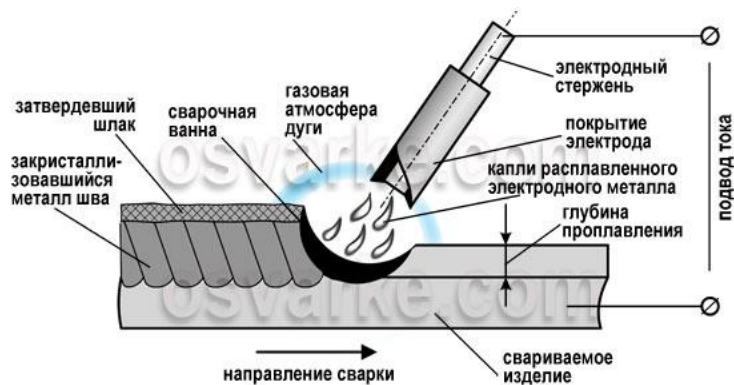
Принципиальная схема ручной дуговой сварки
